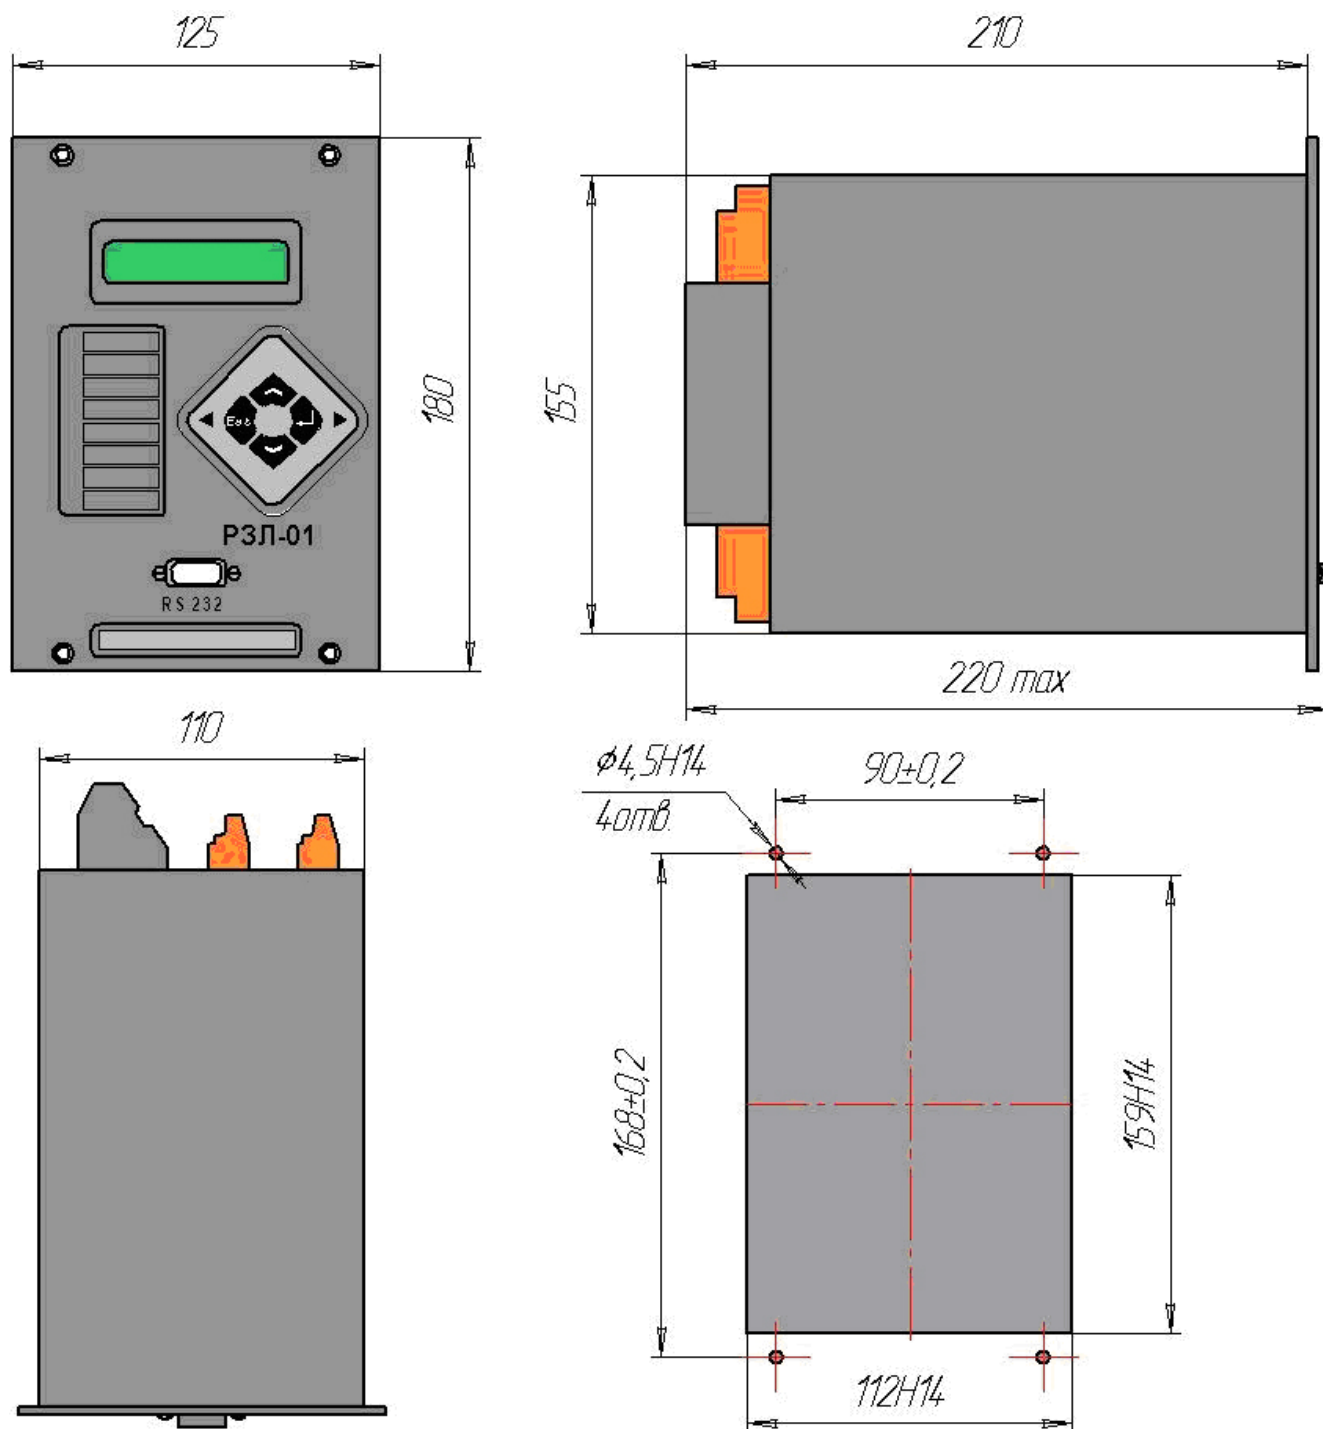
Устройство РЗЛ-01. Габаритные и установочные размеры.
